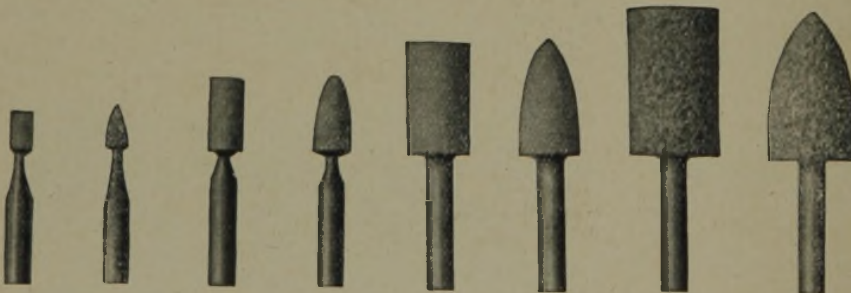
Rotor-Einheitsschleifstifte für Biegsame-Welle-Maschinen
